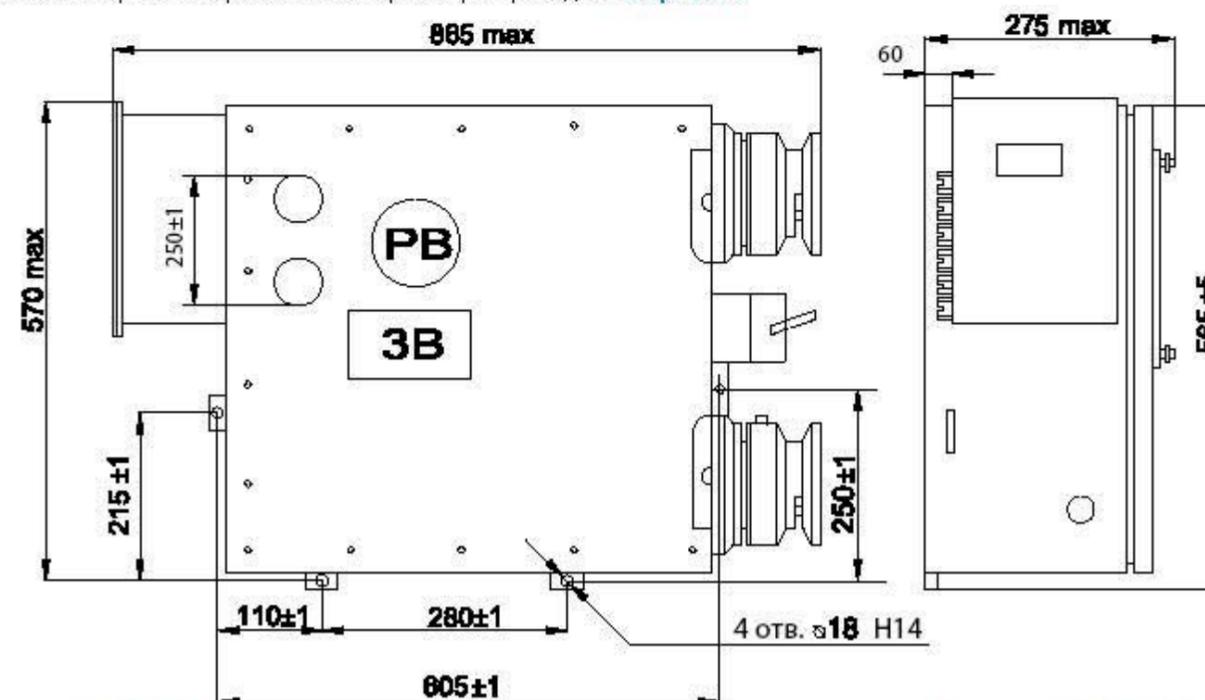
Габаритные и установочные размеры выключателя рудничного взрывобезопасного ВРВ-150М2
